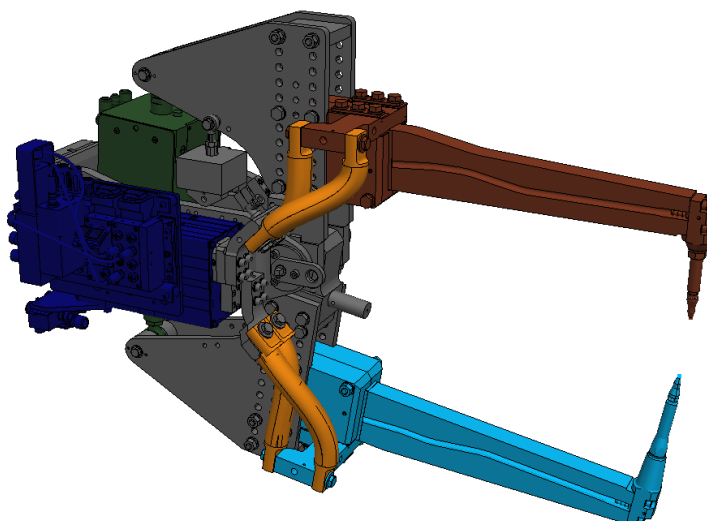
Сварочный пистолет для робота 5080R03 тип X
